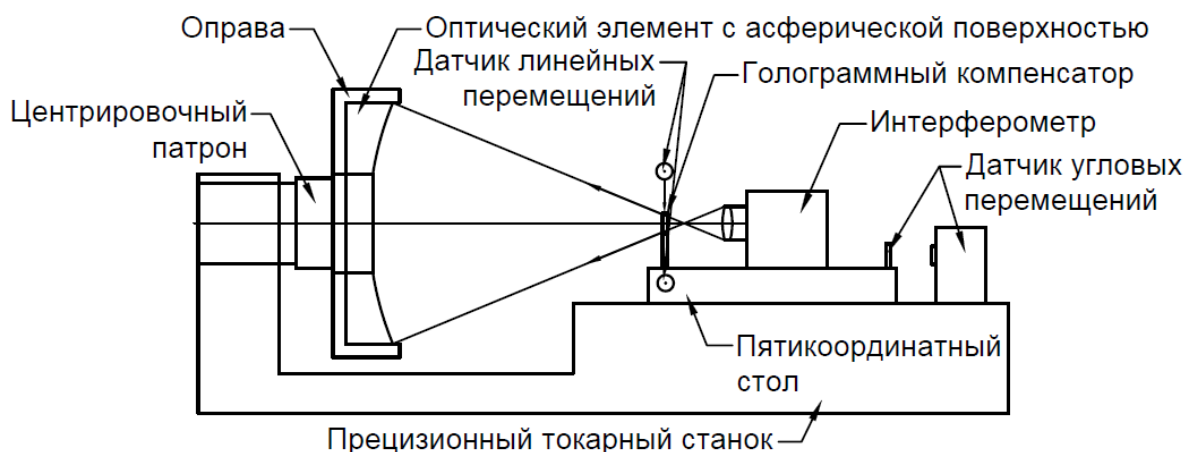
Схема интерферометрического способа центрировки асферической поверхности в оправе
